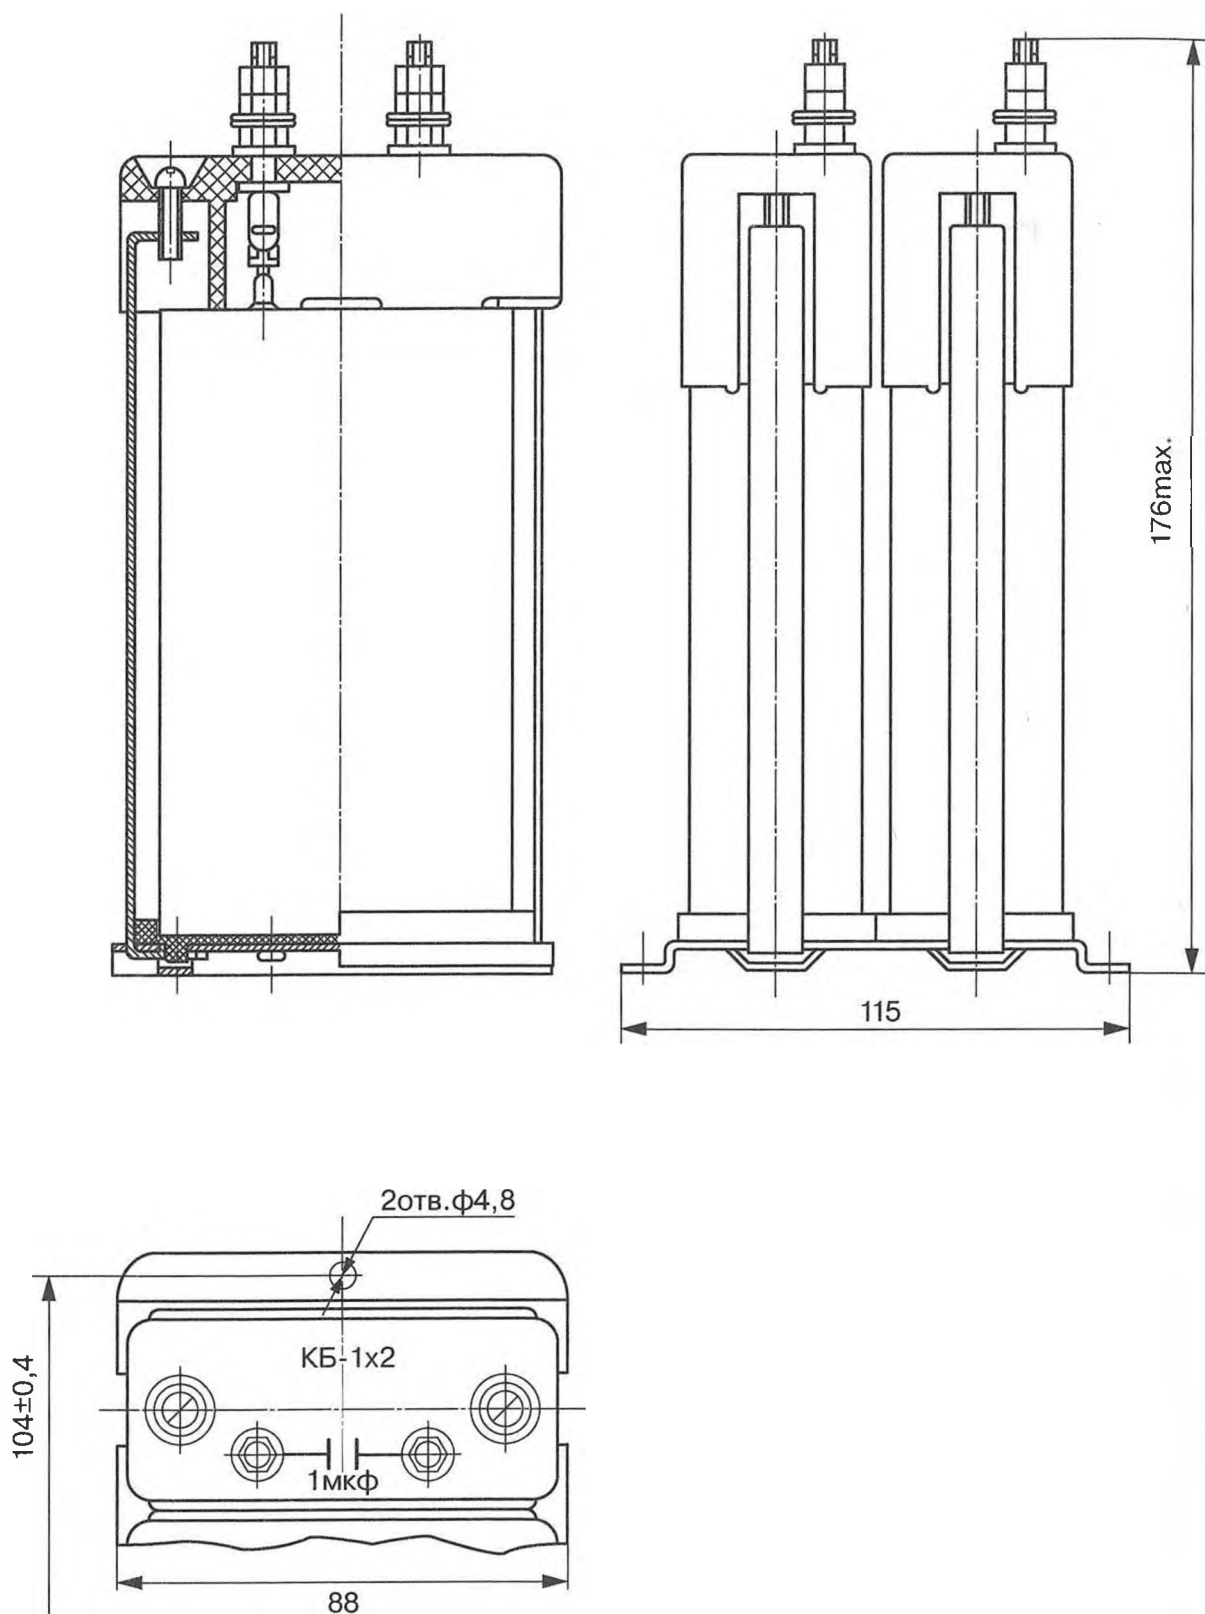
Габаритные и установочные размеры блока конденсаторного KB-1x2
